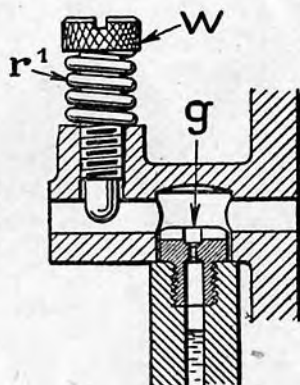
Carburateur FH à starter. Coupe par la vis de réglage d'air du ralenti.
